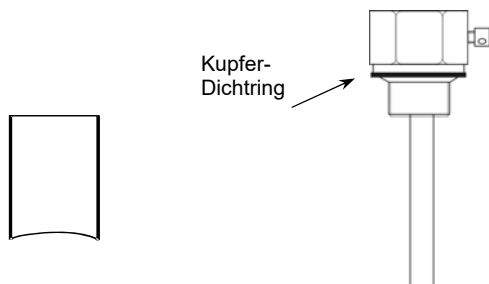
Schweißmuffe Abb. 7: Edelstahl-Tauchhülse
